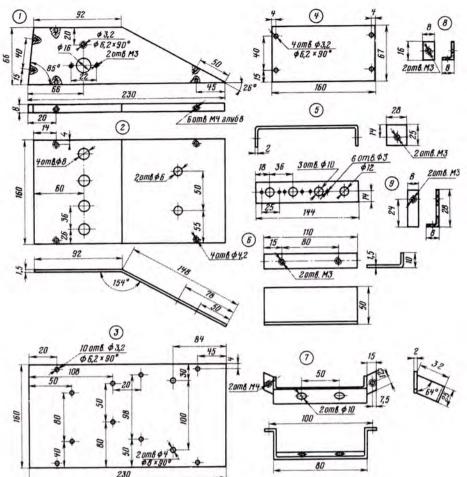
Детали корпуса приставки. 1- боковая стенка, гетинакс, 2 шт.; 2- верхняя крышка, дюралюминий Д16AT; 3- дно, дюралюминий АМГ; 4- задняя крышка, дюралюминий АМГ, 5- скоба, дюралюминий АМГ; 6- перегородка, дюралюминий АМГ; 6- кронштейн, сталь 10; 8, 9- уголки крепления плат, 2 шт., дюралюминий АМГ.
